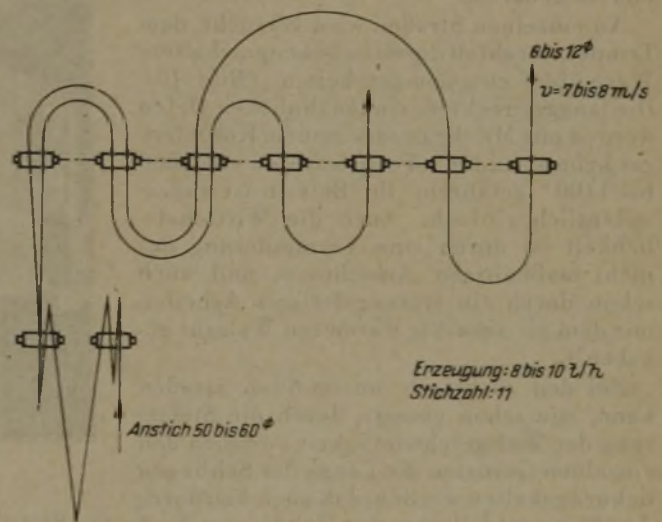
Gerüstanordnung für die Arbeitsweise mit zwei Fertigoval- und zwei Fertigerundgerüsten.
